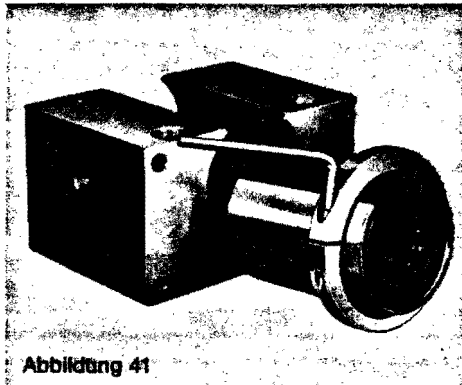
Montagegering (Bestellnummer 0940-0...00) ist an die STAR-*Radial-Kugelbüchse* angebracht und so weit einengend, bis sie sich von Hand in die Gehäusebohrung einschieben läßt. Die Bohrung des Montagegerings muß um ca. 0,5 größer als der Außendurchmesser „D“ der STAR-*Radial-Kugelbüchse* sein.
